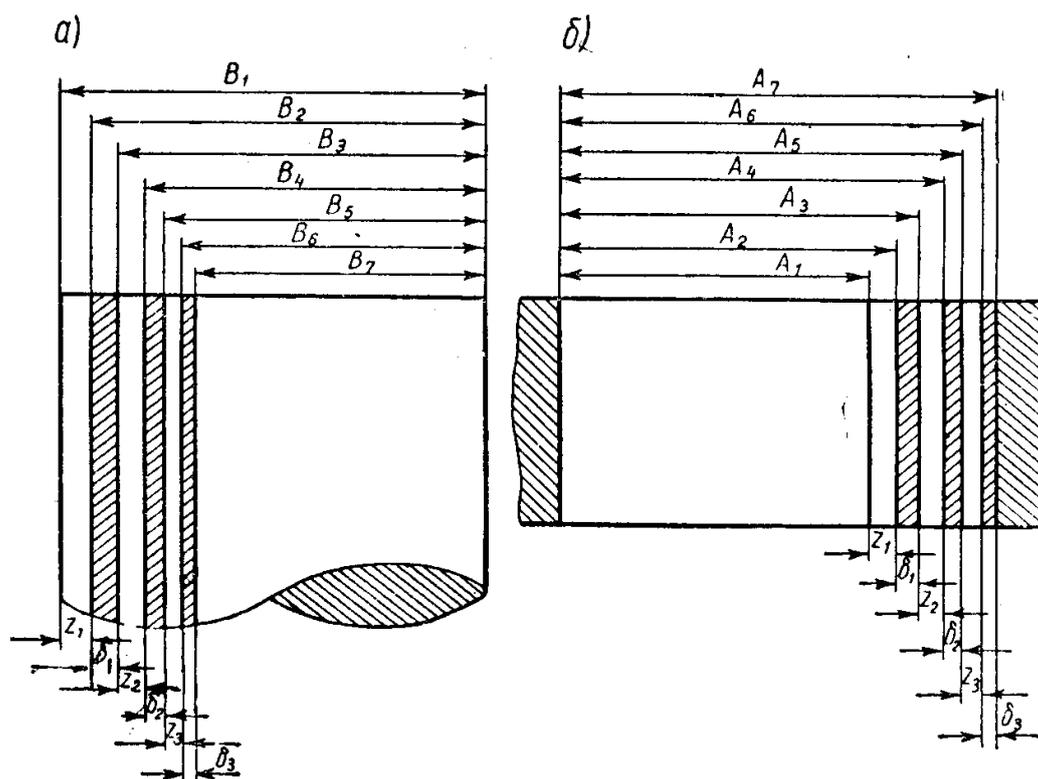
Схема расположения межоперационных припусков и допусков:
